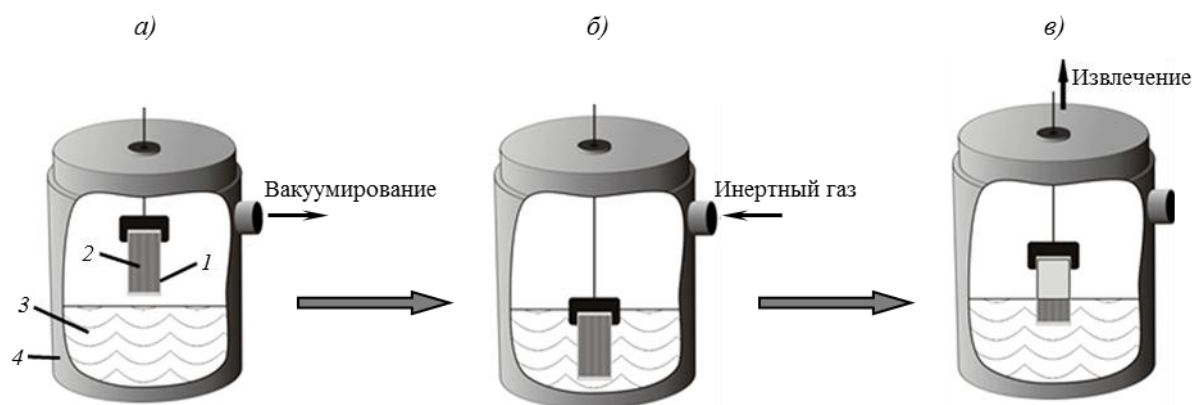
Схема вакуумно-компрессионной пропитки заготовки с погружением в расплав алюминиевого сплава:
